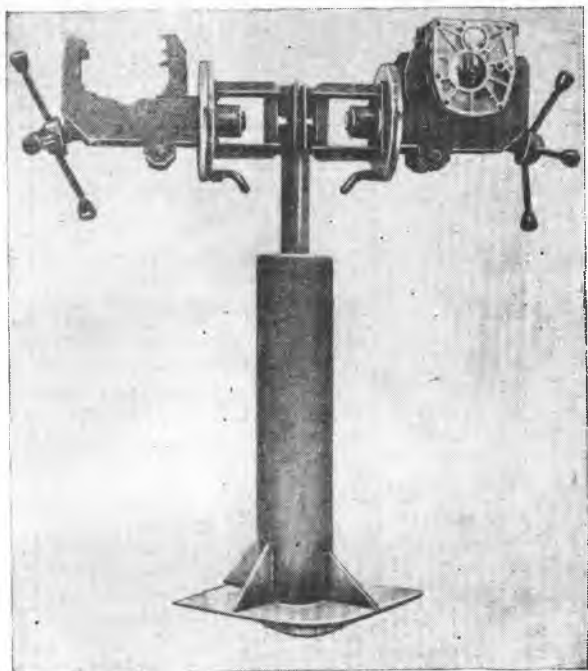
Стенд БС-09-000 для разборки коробки передач
